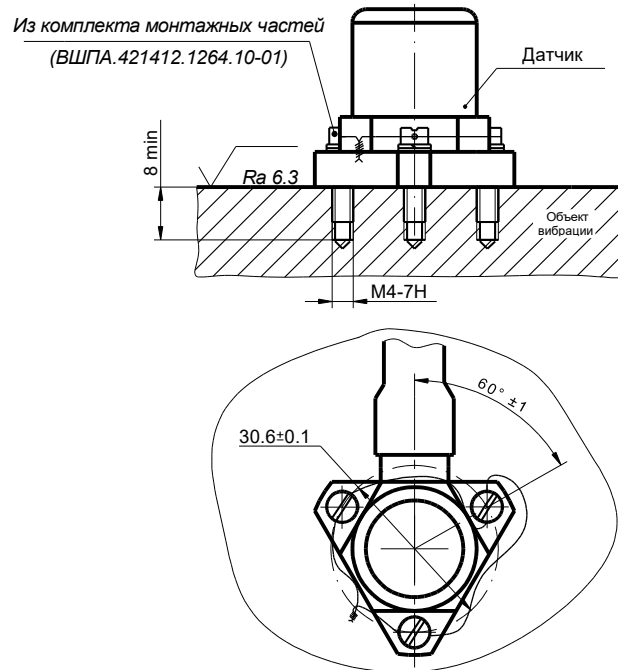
Установка датчиков с корпусом типа ТЗМ4
